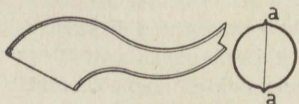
Abb. 369-und 370. Schweißen eines Hohlkörpers.
